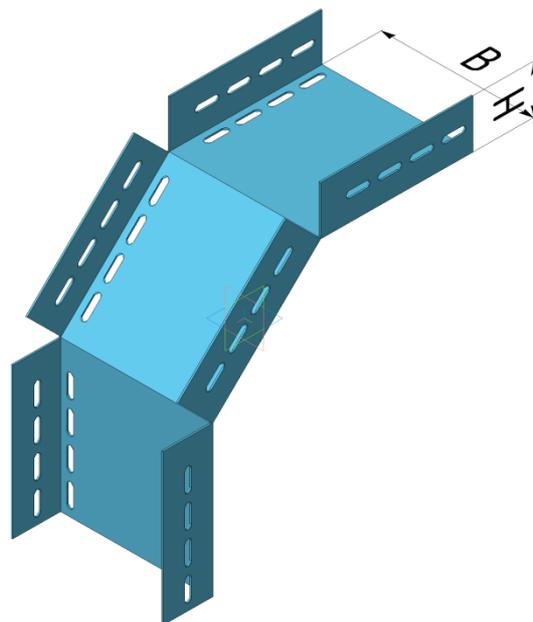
Лоток угловой для поворота трассы вниз под углом 90° типа ЛПН-90. Общий вид
